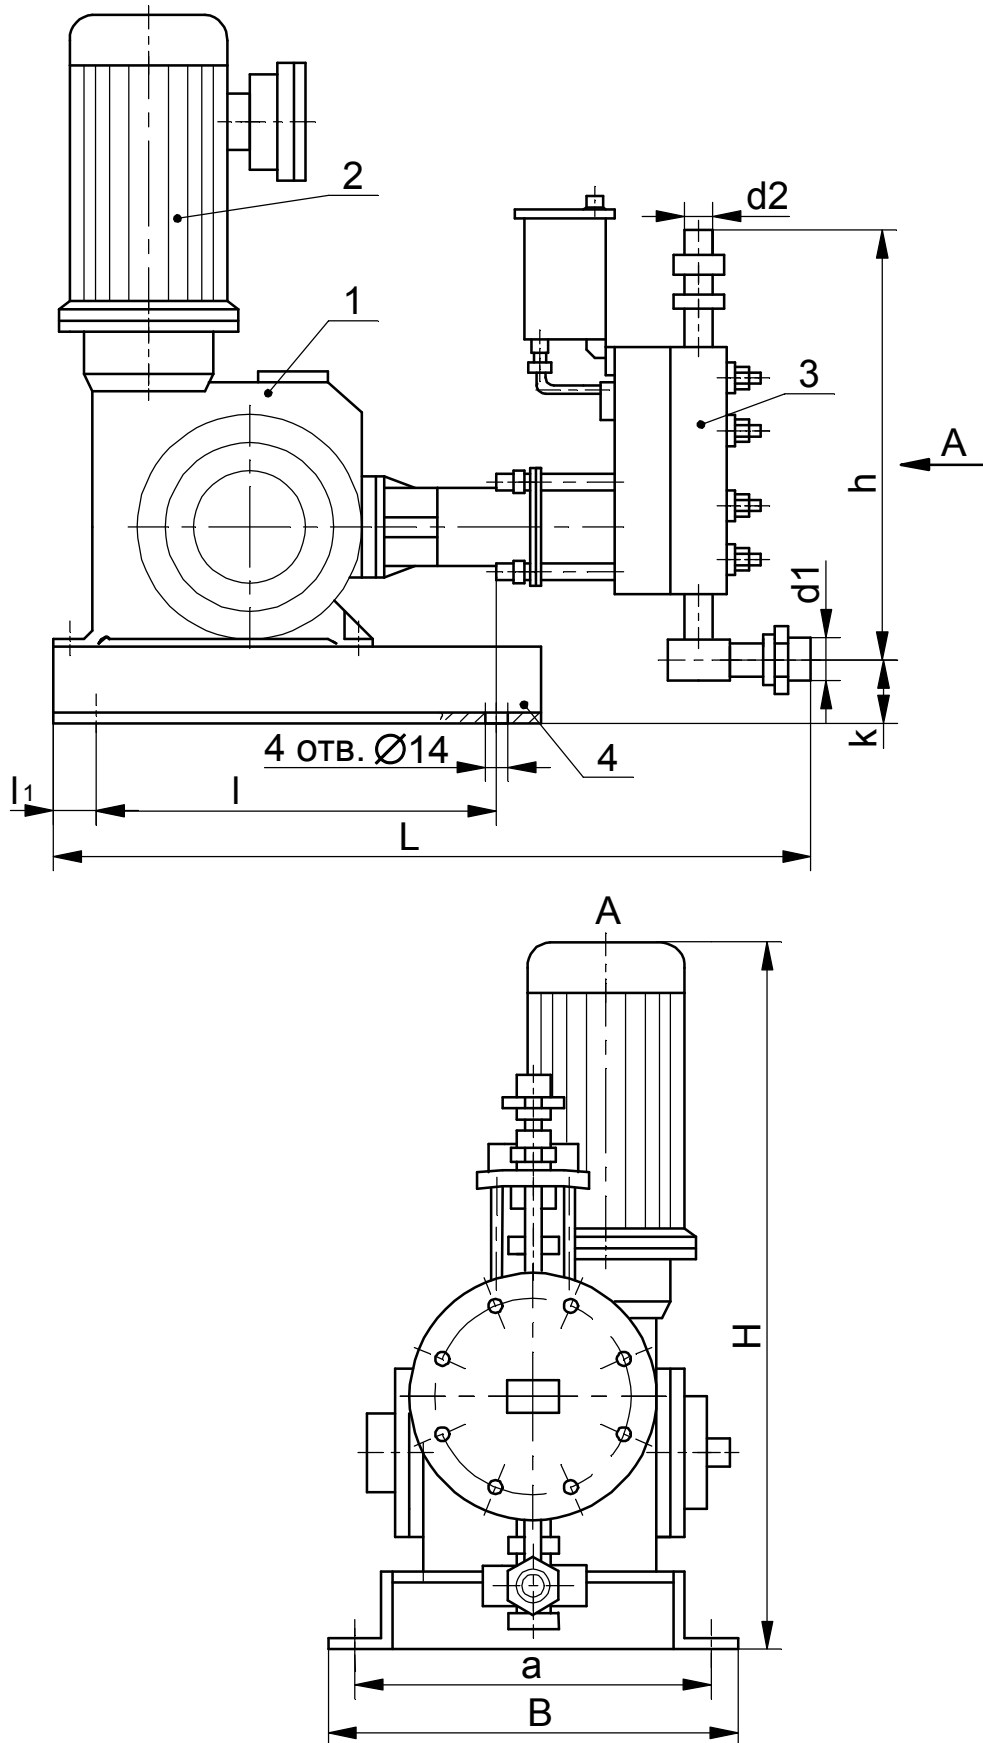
Внешний вид агрегата с параметрами номинального режима 16/63; 40/40; 100/40 и 160/25. Габаритные и установочные размеры
